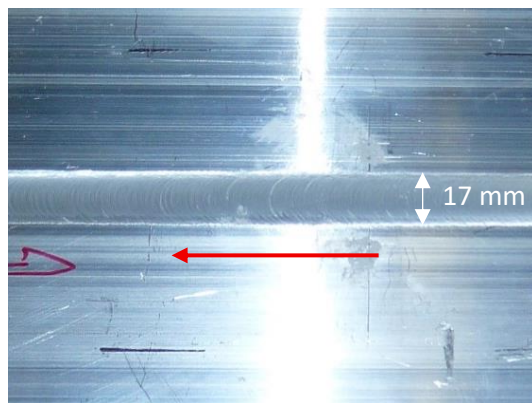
Photographie de la surface supérieure de la soudure T1 (outil B, 800 tr/min, 400 mm/min)
